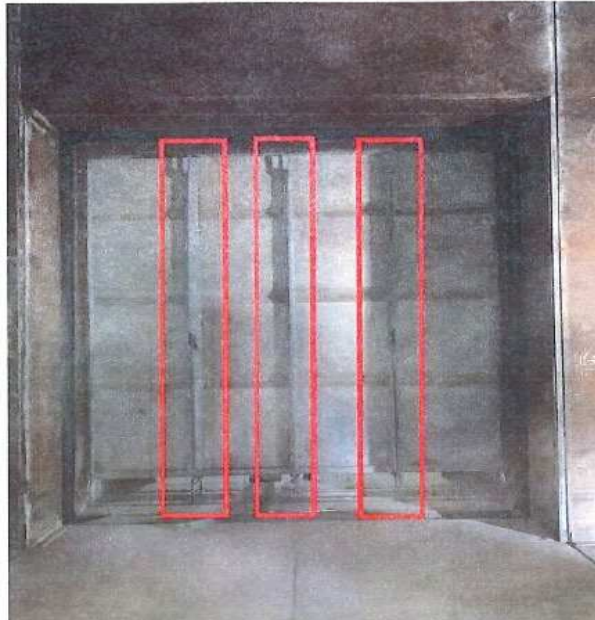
Condición del engranaje del clasificador rotatorio
